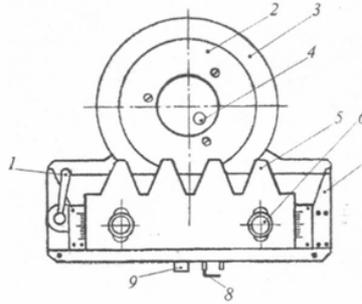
Прибор-резиометр: 1 — рычаг; 2 — накладка; 3 — диск; 4 — винт; 5 — рейка; 6 — винт; 7 — общая панель; 8 — г-образная рукоятка; 9 — клавиша
